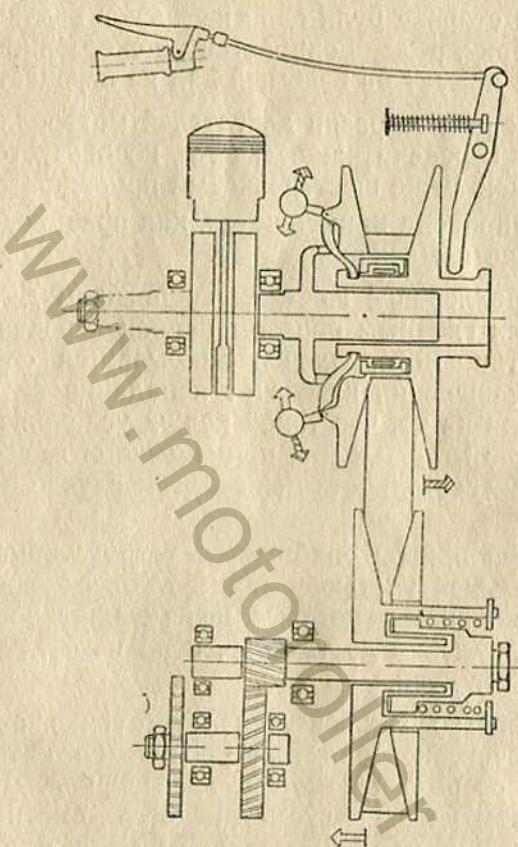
Схема бесступенчатой коробки передач мотороллера «ДКВ-Гобби».
